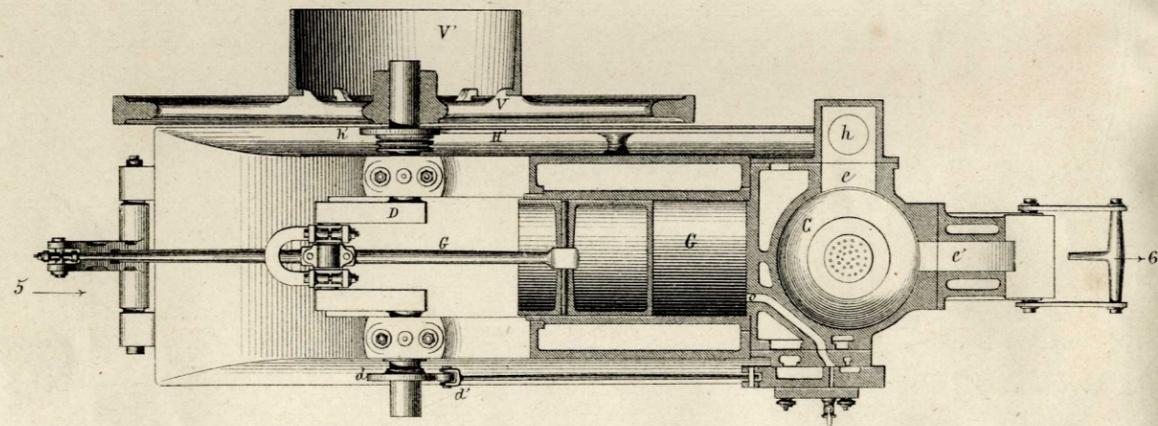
Sezione orizzontale secondo 1, 2.
